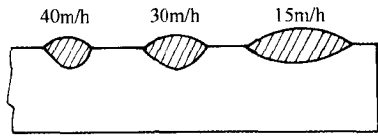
焊接速度对焊缝尺寸的影响
